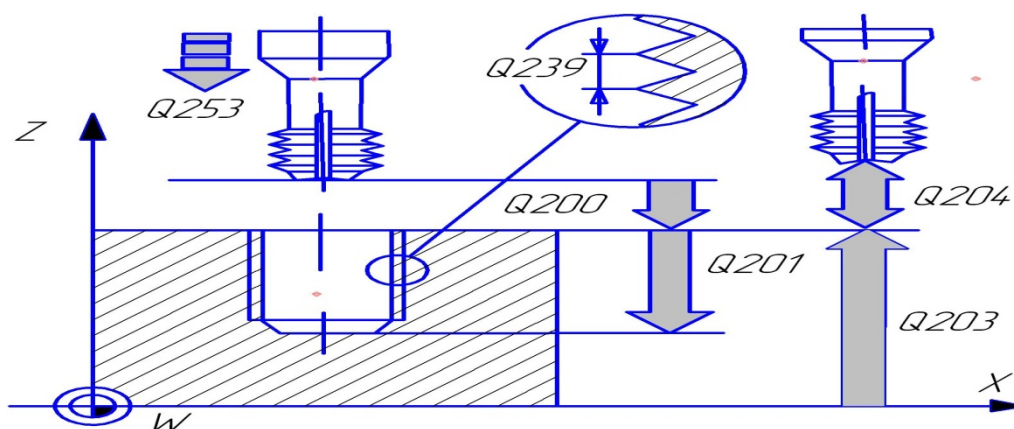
Схема helix-фрезерования резьбы (цикл 265)
